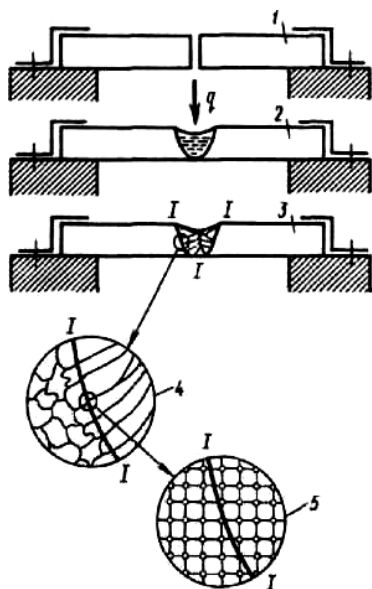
Схема стадий образования соединения сваркой плавлением: 1 – сборка под сварку; 2 – образование сварочной ванны под воздействием источника теплоты; 3 – кристаллизация ванны с образованием сварного соединения; 4 – макроструктура зерен на границе шва; 5 – «стыковка» кристаллических решеток на границе плавления»
